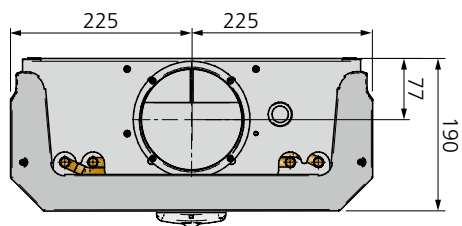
Dimensions ADRIATIC AWC Prisma, vue arrière du raccordement aéraulique
